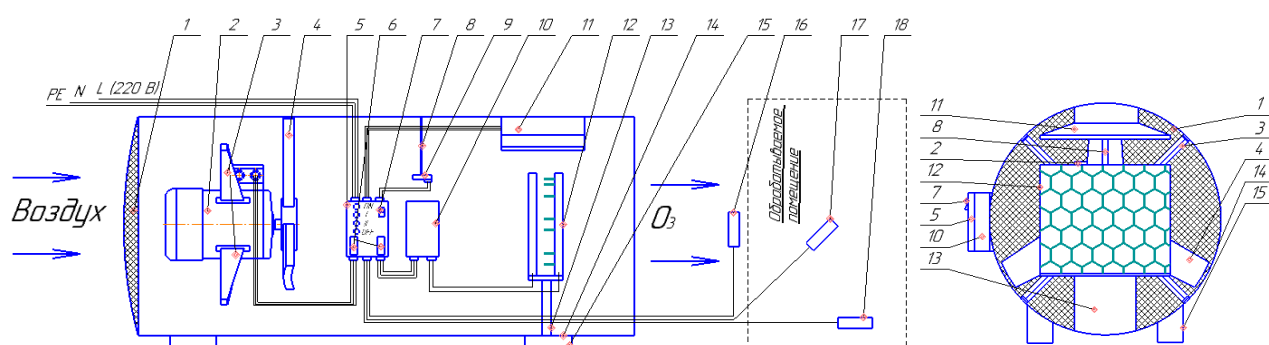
Схема разработанной конструкции озонатора-излучателя
